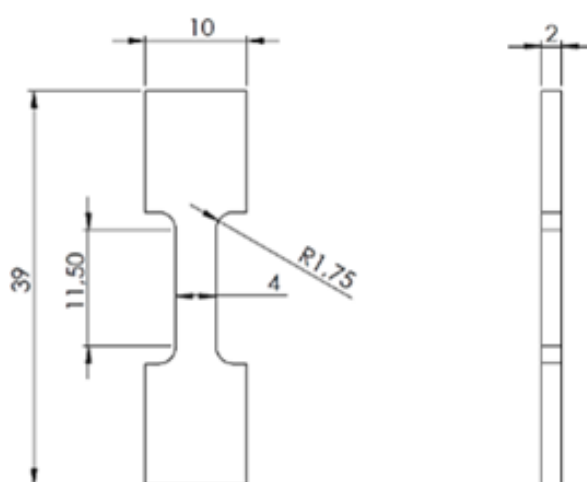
Geometria e dimensões do corpo de prova de tração (dimensões em mm).
